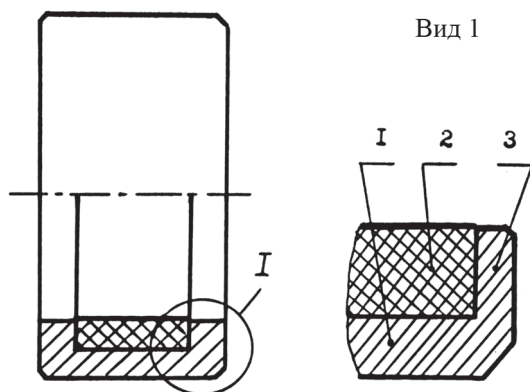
Общий вид втулки шарнирного подшипника технологического оборудования после изготовления: 1 – основа втулки; 2 – УУКМ; 3 – бурт
